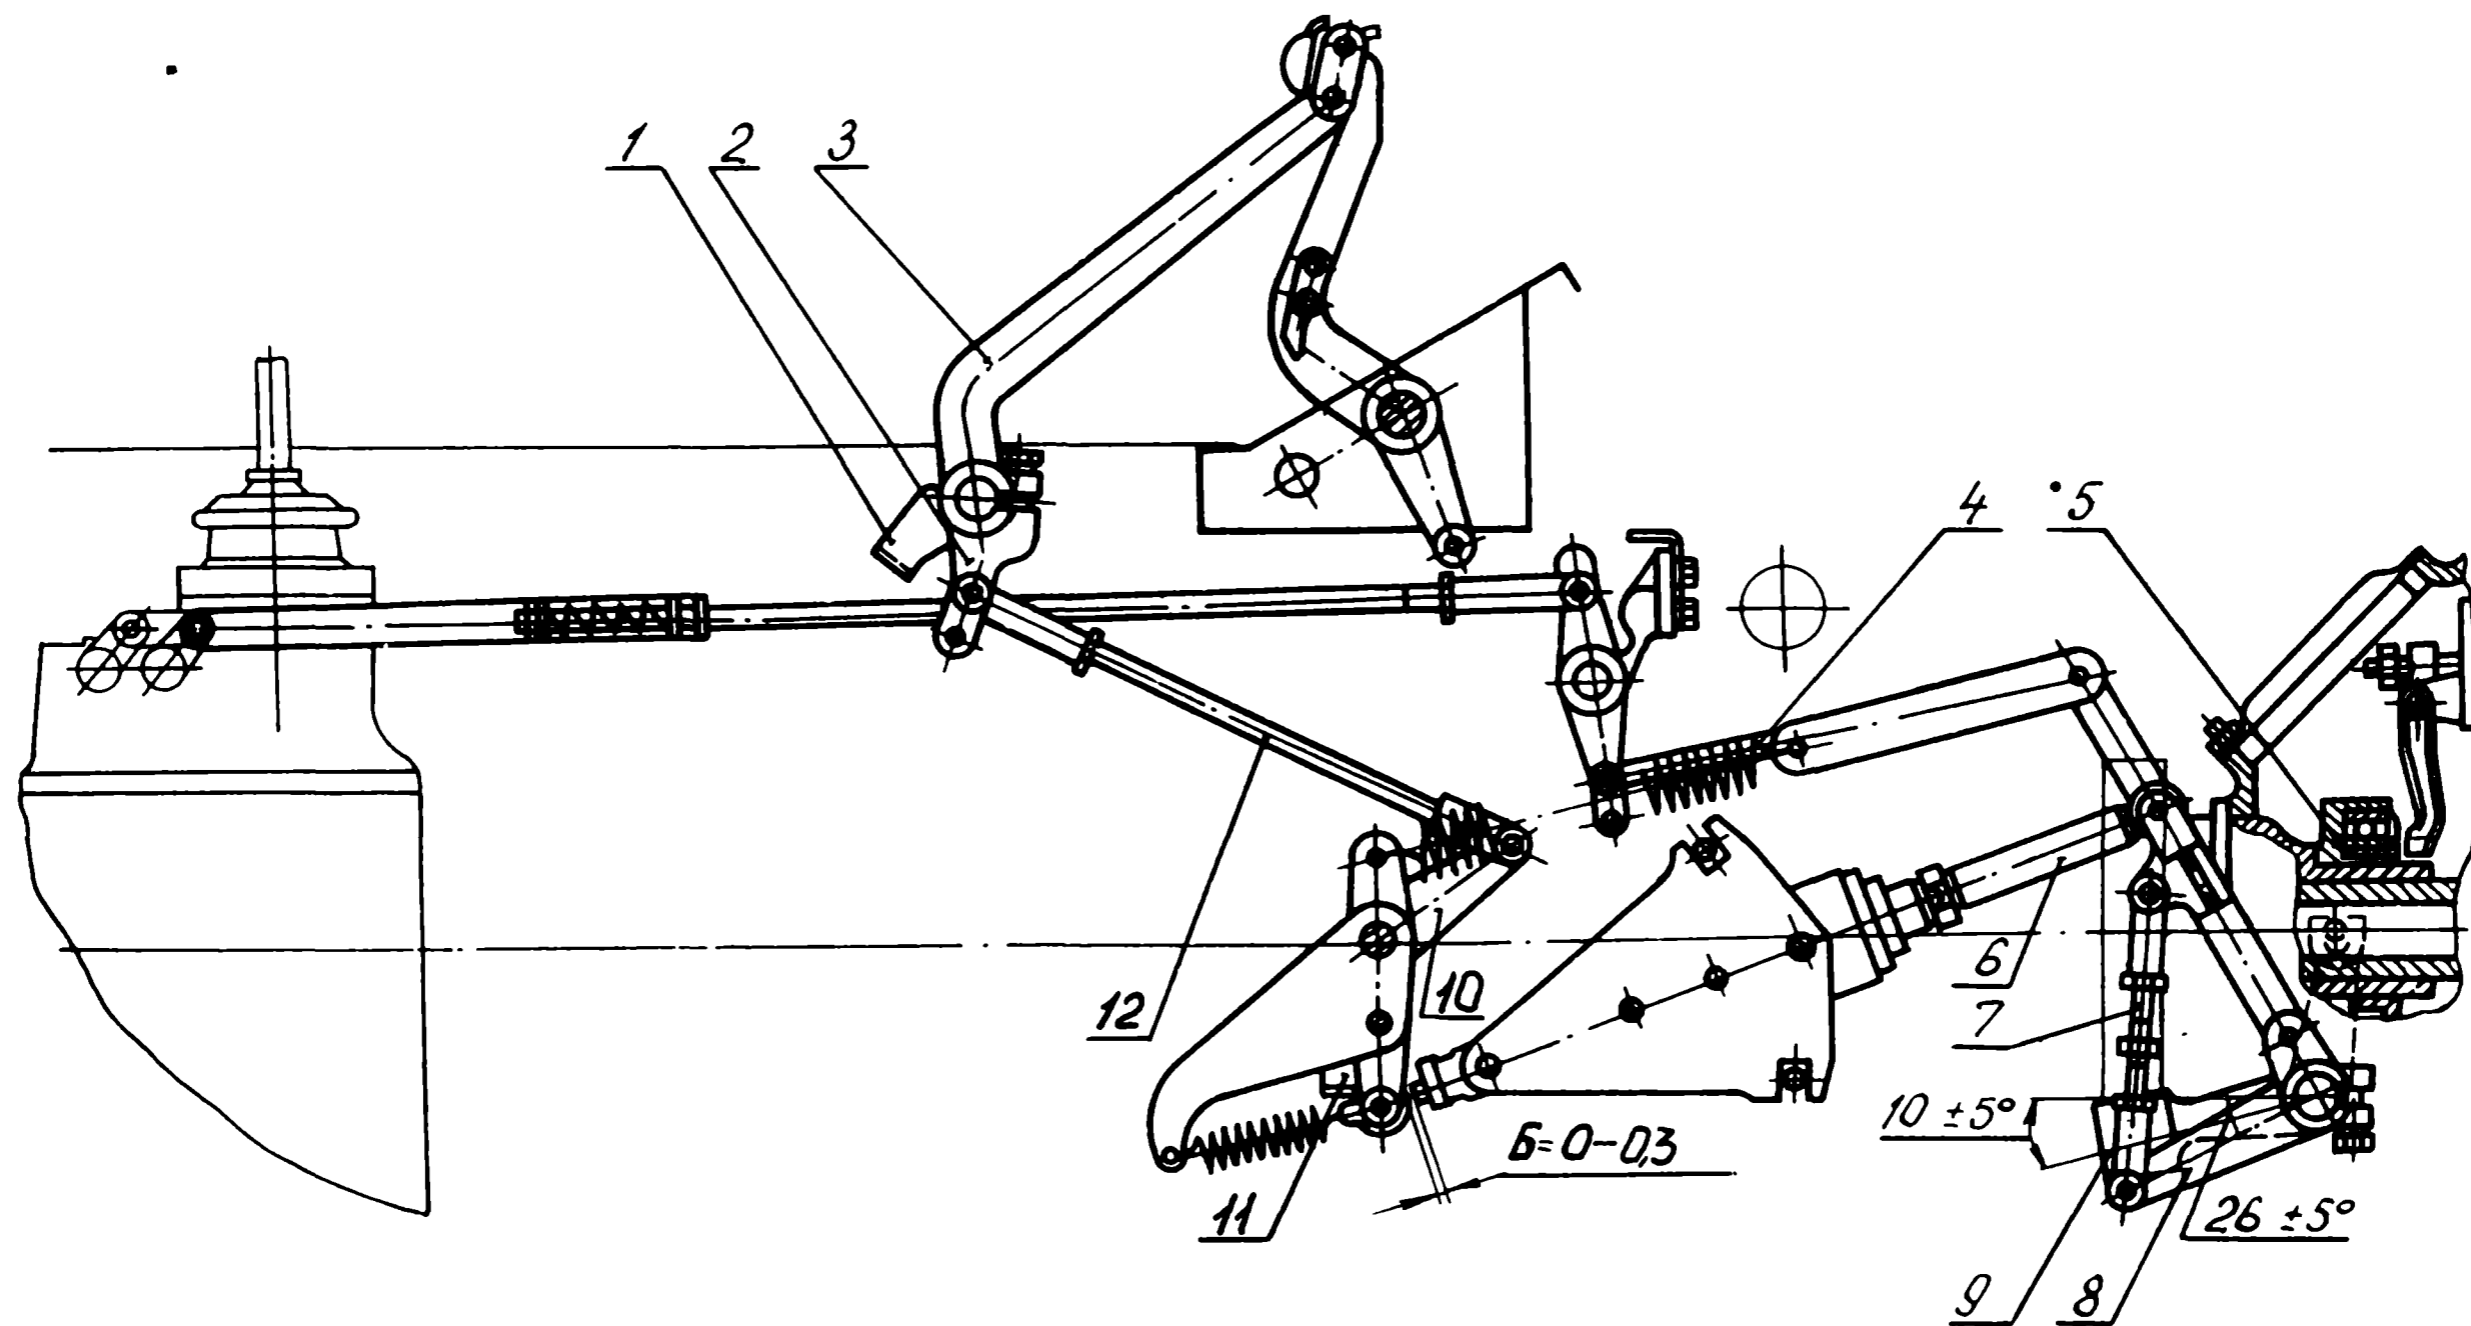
Сборка и регулировка механизма управления главной муфтой сцепления:
